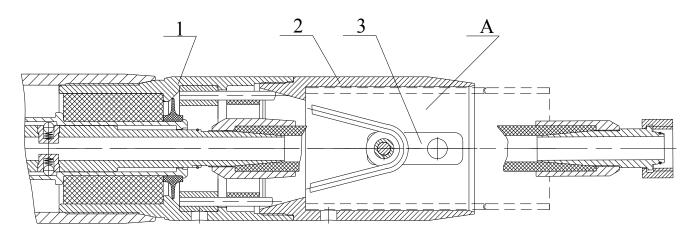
Схема сборки пробойника ИП 4603AM (по заказу) 1 – гайка (ИП 4603.00.501); 2 – Стакан (ИП 4603A.00.502); 3 – серьга
